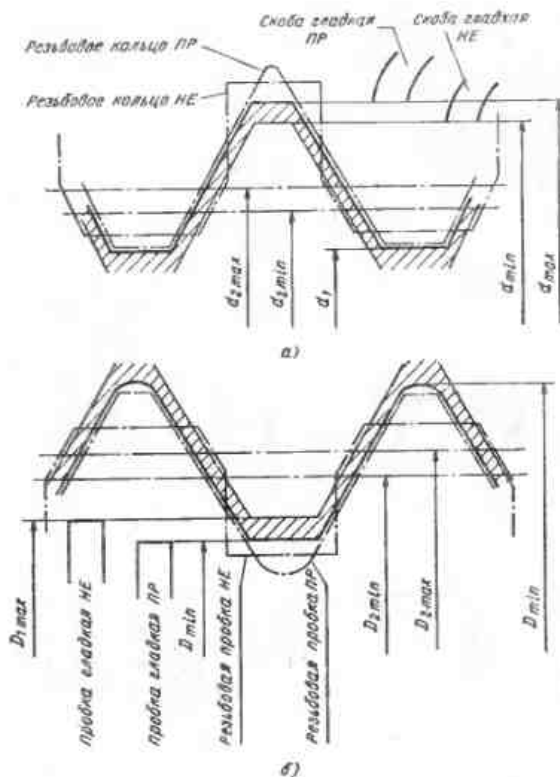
Схема проверки резьбы калибрами: а — болта; б — гайки
